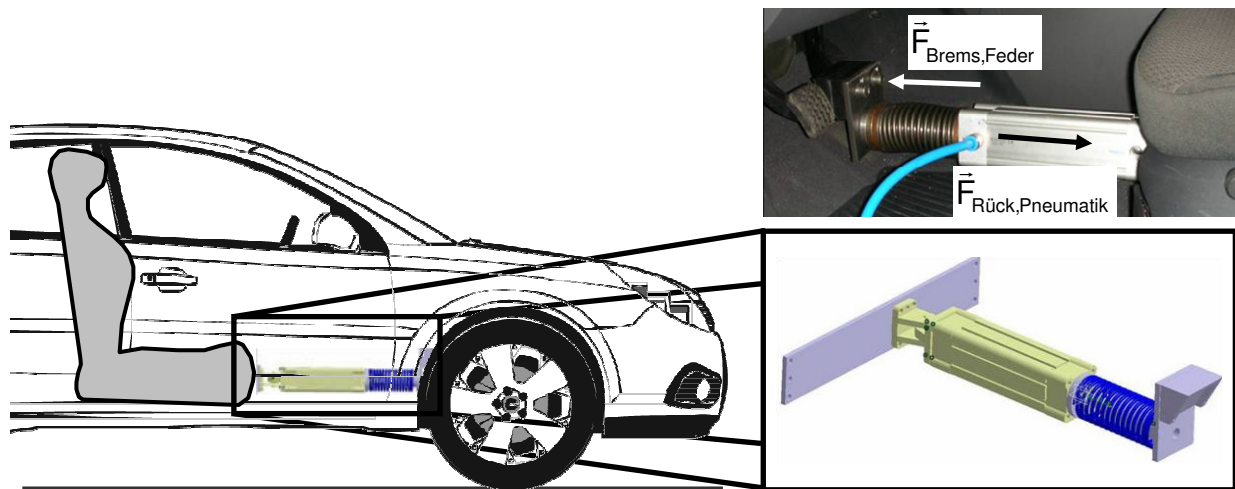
Automatisches Bremssystem mit Pneumatikzylinder und Druckfeder
